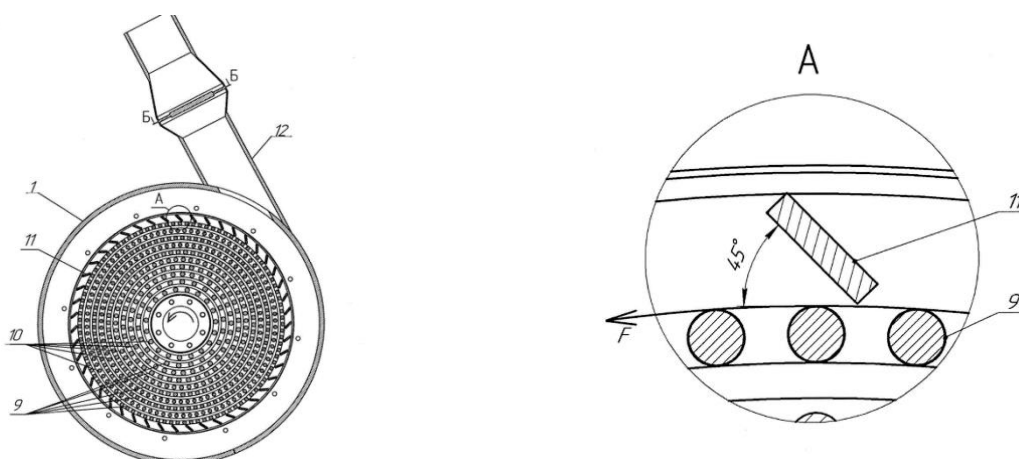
Дезинтегратор: 1 – цилиндрический корпус; 9 – ряд пальцев статора; 10 – ряд пальцев ротора, 11 – пластины, 12 – выгрузочный патрубок
